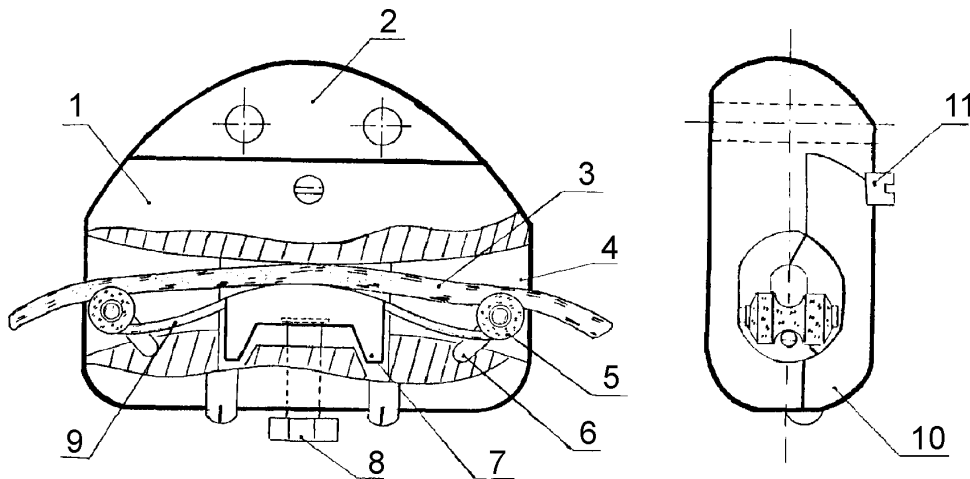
Затискач підтримувальний комбінованого типу з амортизатором для підвішування самонесучого ОК: 1 – корпус затискача; 2 – елемент кріплення корпусу до опори; 3 – ОК; 4 – отвір вводу-виводу ОК; 5 – ролик підтримки ОК; 6 – пази для встановлення роликів; 7 – планка пересувна; 8 – болт затискний; 9 – пружина натискна поздовжня; 10 – кришка відкидна; 11 – болт для затиску кришки
